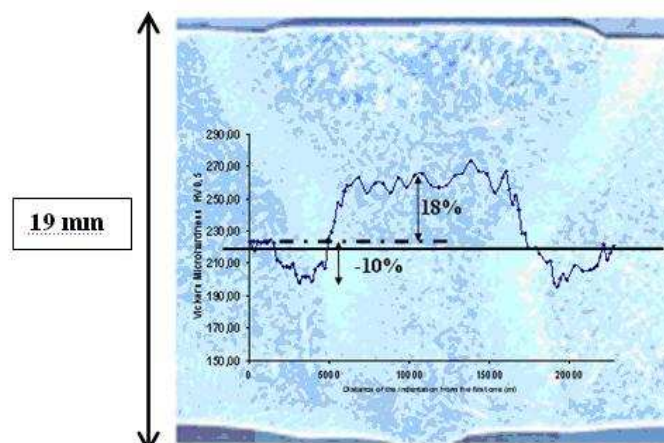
Profil de microdureté superposé à une macrographie du joint soudé.
